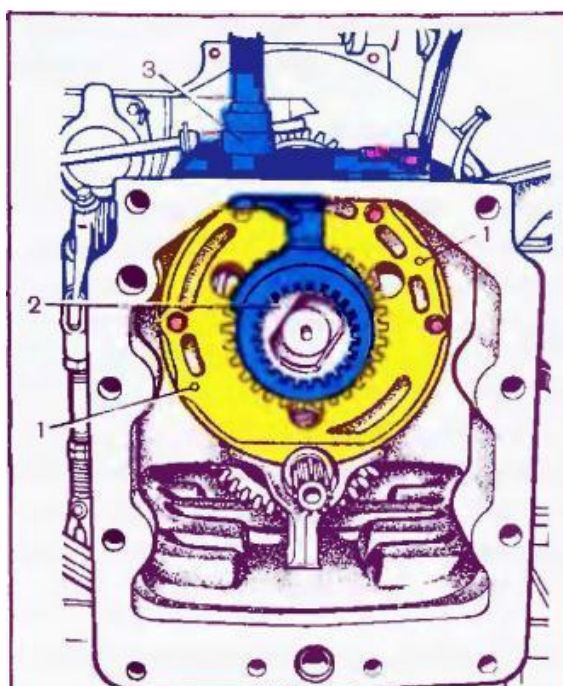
Снятие механизма управления понижающим редуктором МТЗ и зубчатой муфтой; спрессовка вала сцепления
